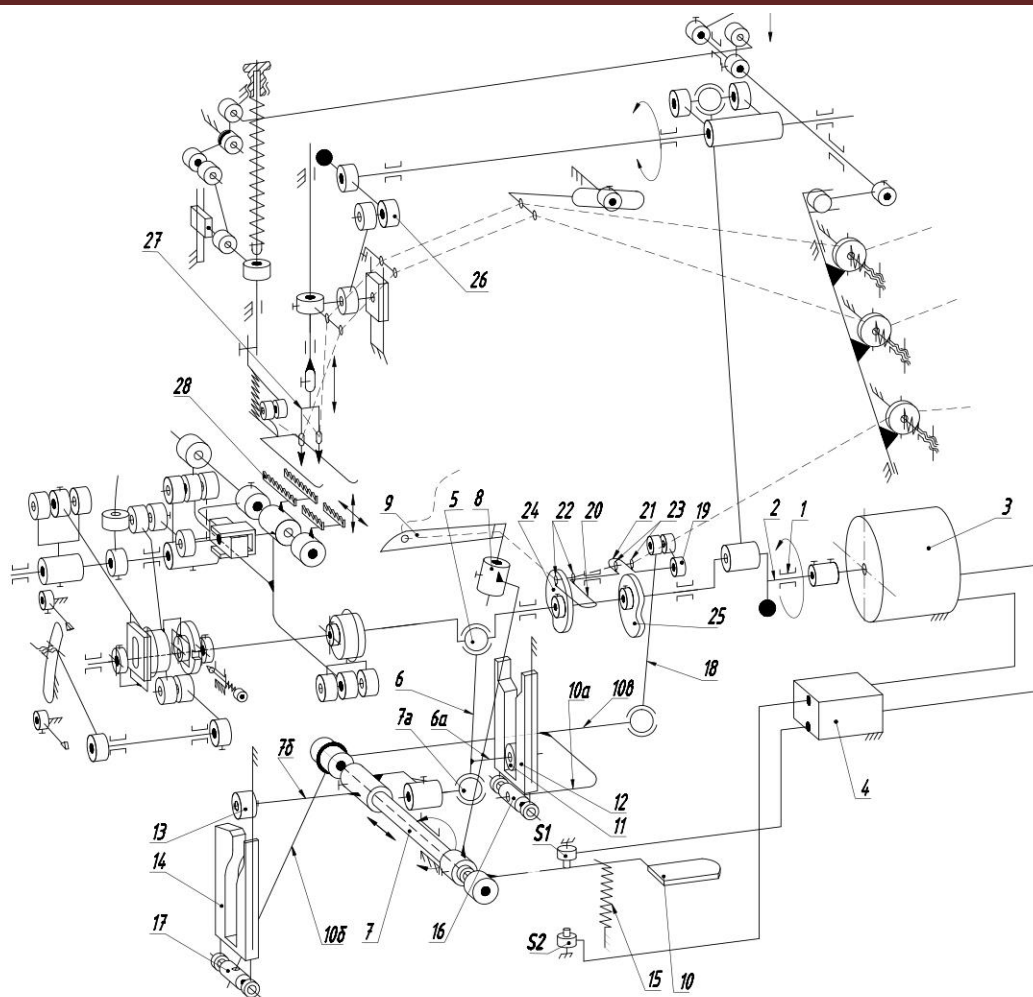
кінематично-принципова схема швейної машини двохниткового ланцюгового стібка з реверсом подачі матеріалів
